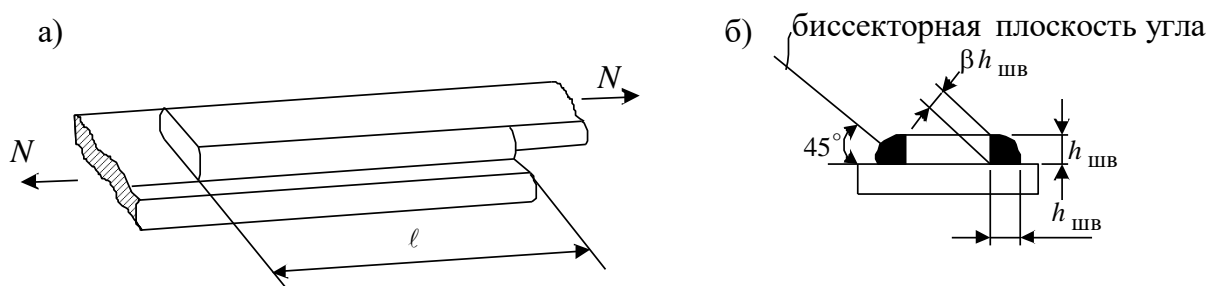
Сварное соединение угловыми швами
